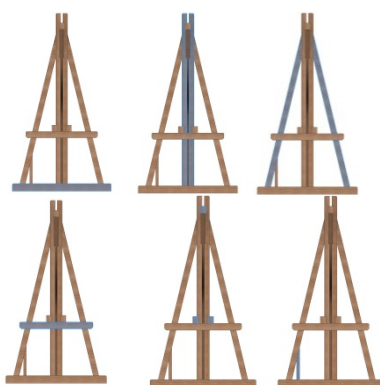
Vista de alzado del soporte de la cuchara: secuencia de montaje.
